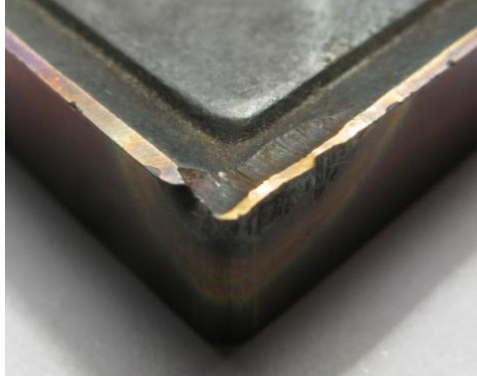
Загальний вигляд зношеної різальної пластини
